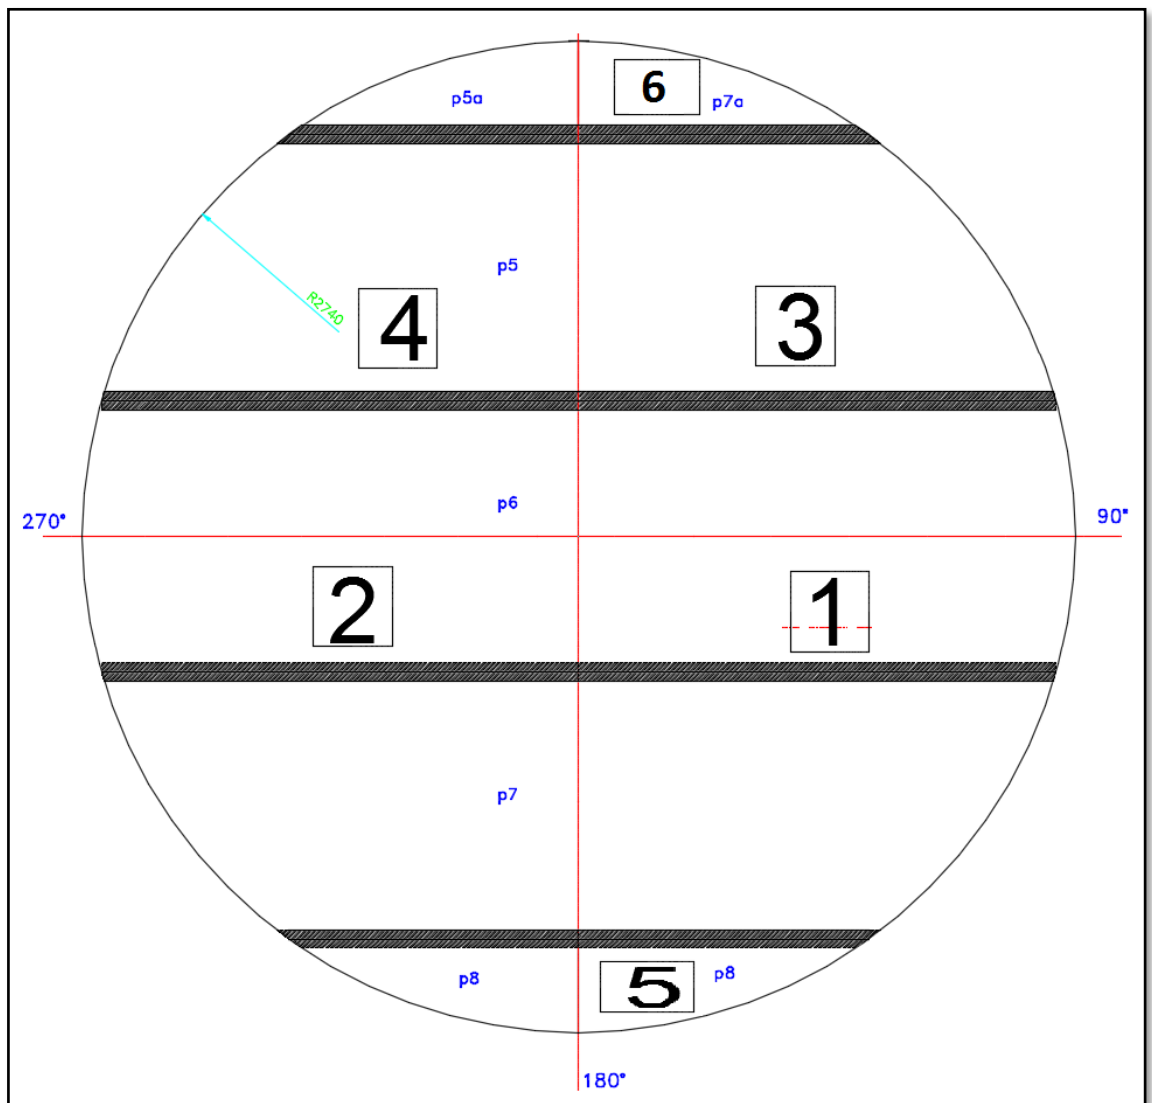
Secuencia del soldeo en horizontal de la Plancha de Fondo.
